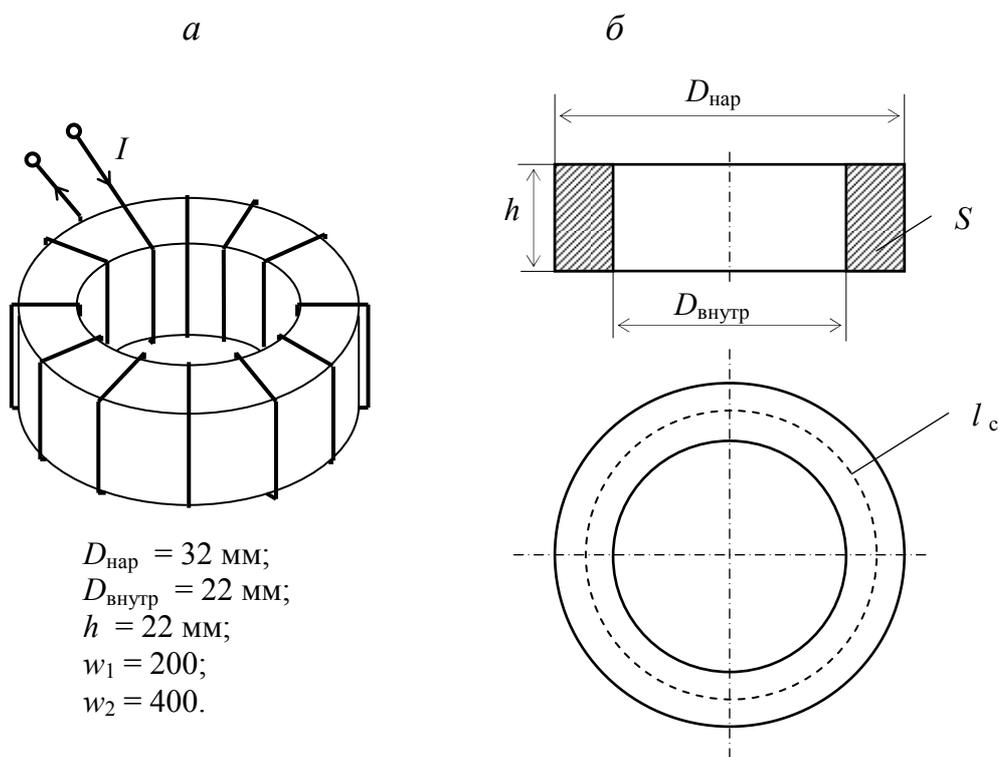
Внешний вид (а) и геометрические размеры (б) тороидального образца из ферромагнитного материала
